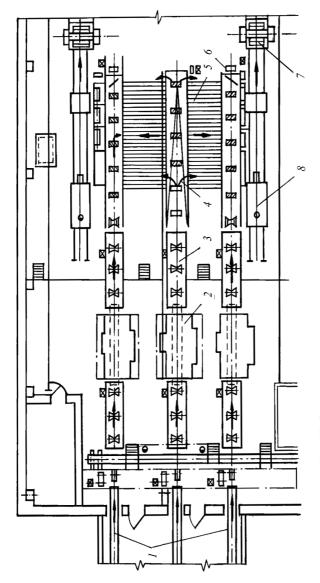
Схема участка окорки в лесоцехе перед лесопильными рамами: I — продольный конвейер; 2 — окорочный станок; 3 — приемный конвейер; 4 — распределительный конвейер; 5 — поперечный конвейер; 6 — роликовые конвейеры; 7 — лесопильная рама; 8 — впередирамная тележка
